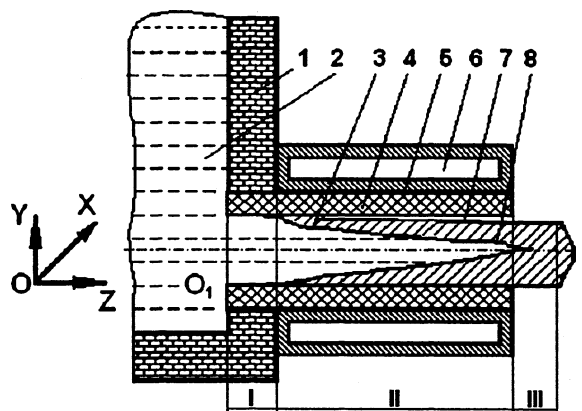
Схема процесса непрерывного горизонтального литья: 1 – металлоприемник; 2 – жидкий металл; 3 – начальная корка; 4 – графитовая вставка; 5 – стальной корпус кристаллизатора; 6 – вода; 7 – зазор между отливкой и графитовой вставкой; 8 – отливка; I – неохлаждаемая зона кристаллизатора; II – охлаждаемая зона; III – зона вторичного охлаждения
